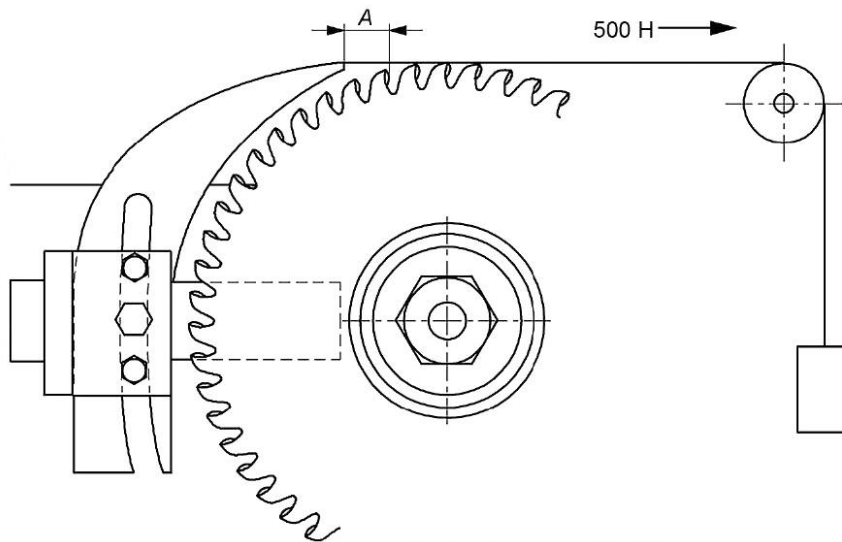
Проверка прочности крепления расклинивающего ножа
